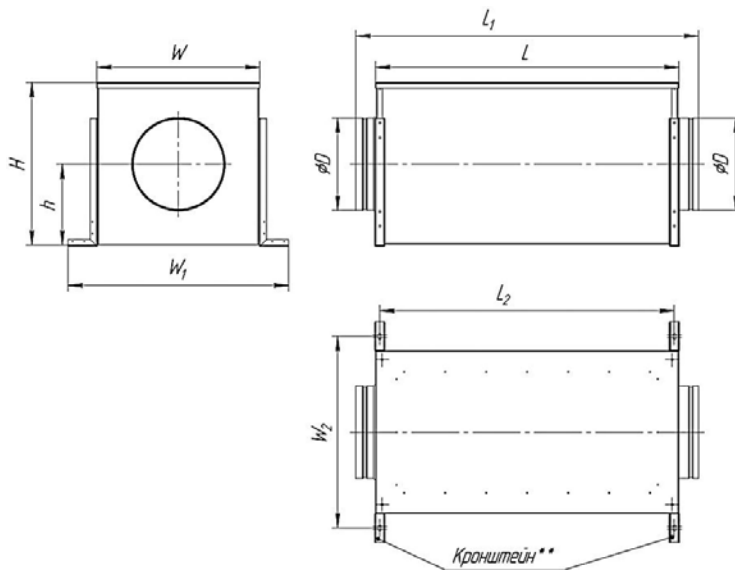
Габаритные, присоединительные и установочные размеры приточной установки МПУ (МРУ). Кронштейн в комплект поставки не входит.
